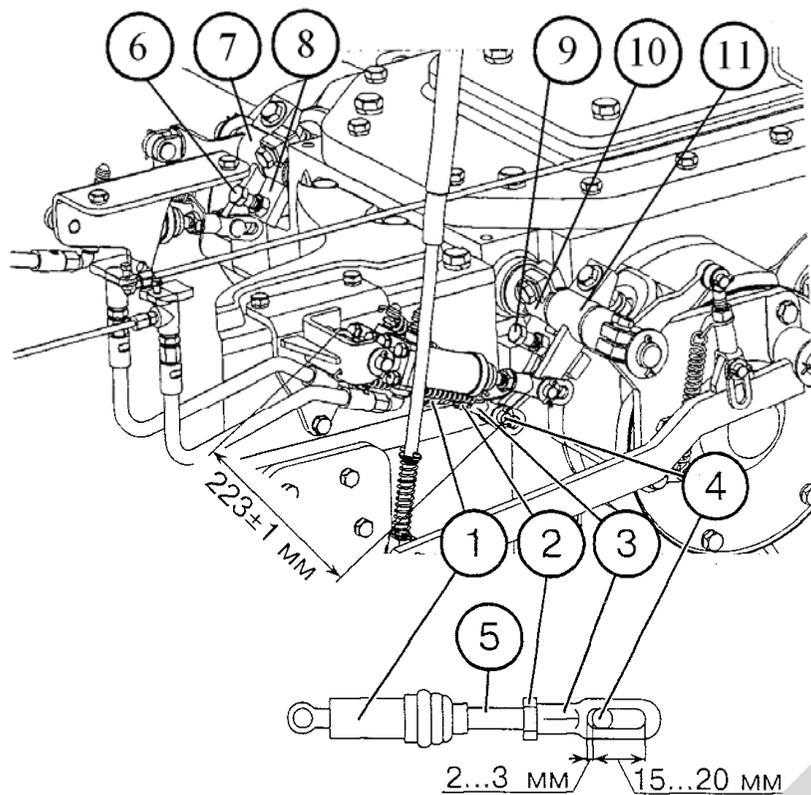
Регулировка свободного хода рабочих тормозов:
